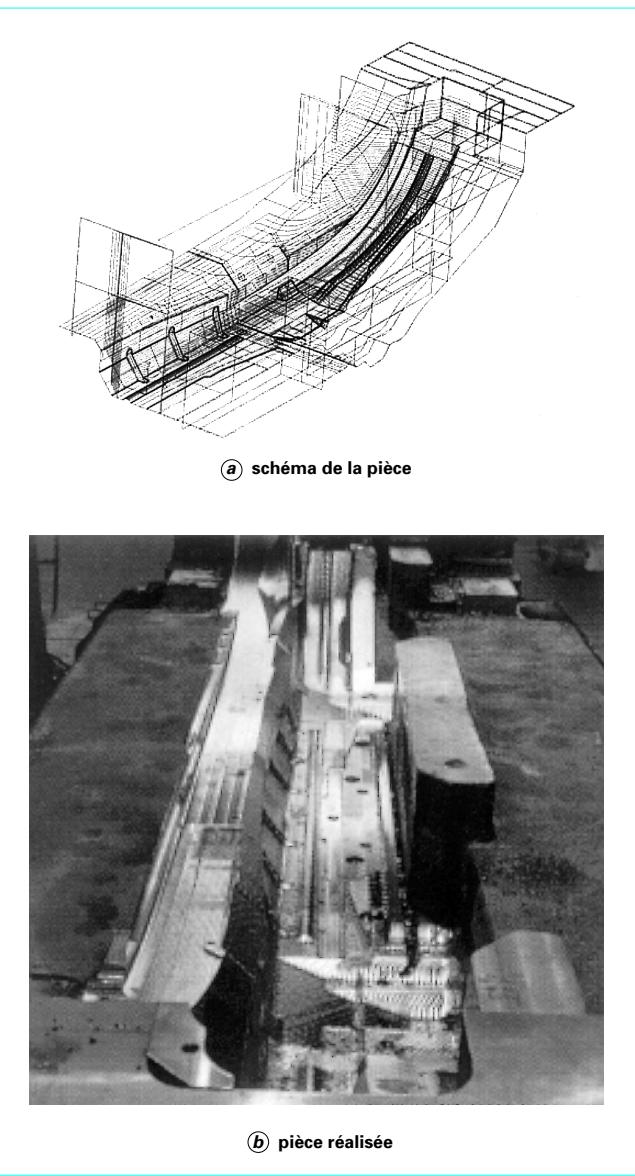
Exemple de pièce de grandes dimensions réalisée sur fraiseuse CNC
